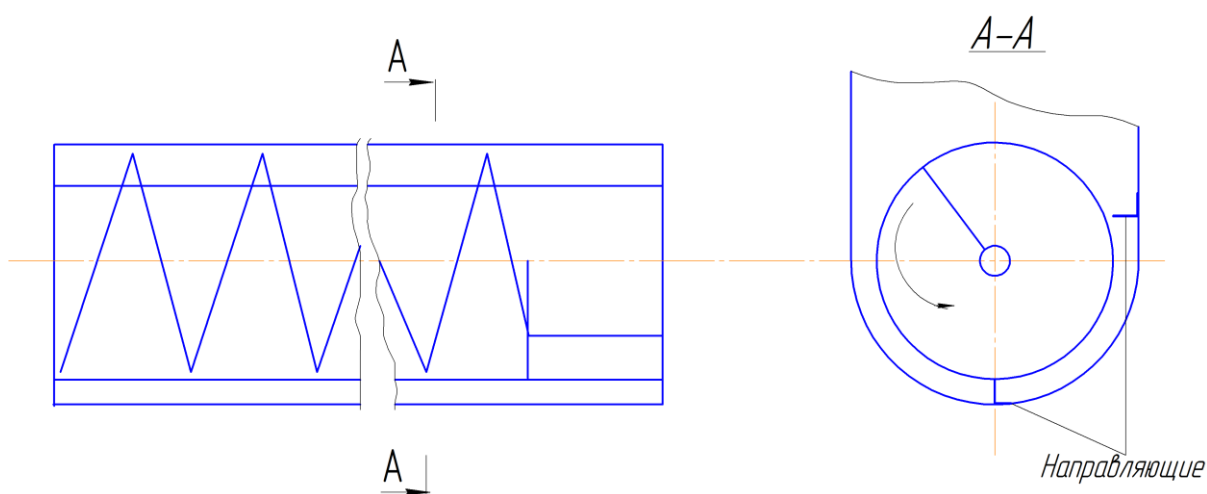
Схема расположения направляющих пластин внутри кожуха выгрузного шнека.
